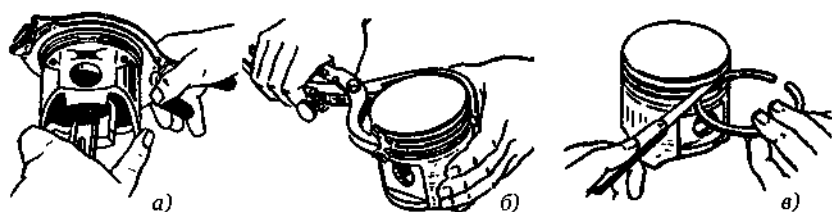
Замена поршневых колец: а — снятие поршневых колец с поршня; б — зачистка канавок для колец; в — проверка зазора
